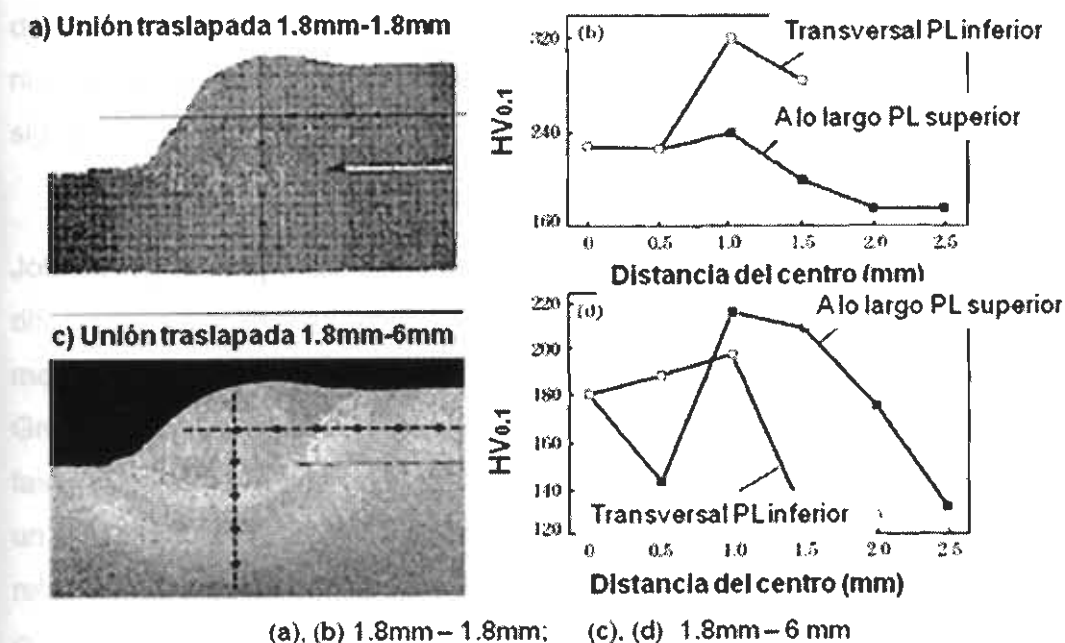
Perfil de soldaduras para soldadura de unión traslapada [13].
